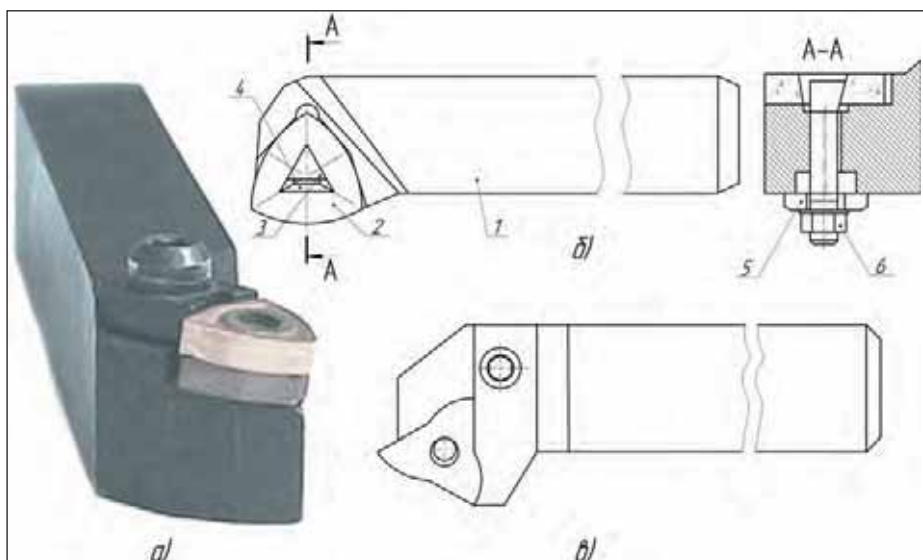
Проходные резцы с режущими пластинами высокой прочности
